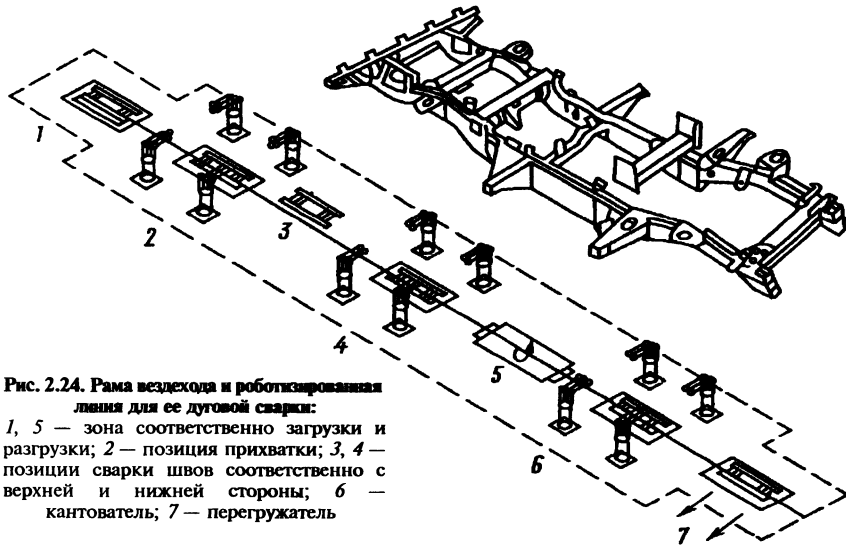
Рама вездехода и роботизированная линия для ее дуговой сварки:
